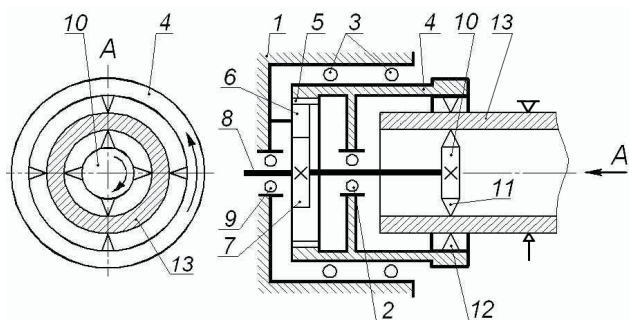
Пристрій для одночасної обробки внутрішньої та зовнішньої поверхонь
